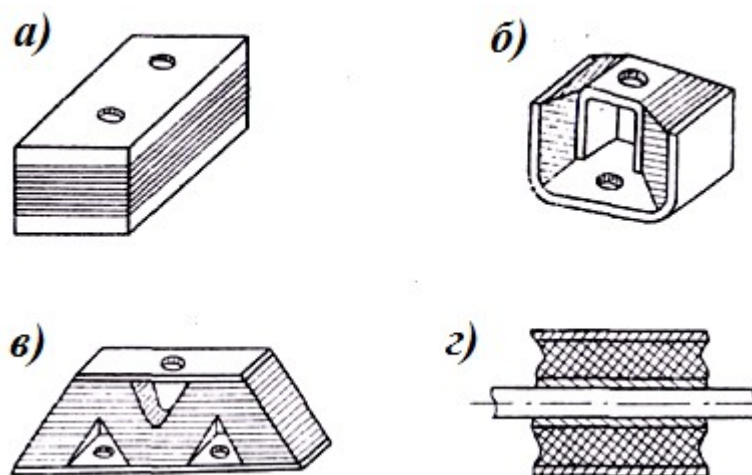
Типовые конструкции сварных резинометаллических опорных виброизоляторов
